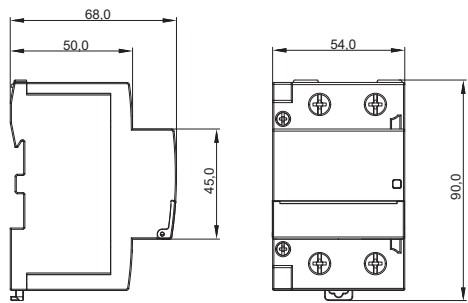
Габаритные размеры контакторов 100 А, 2P / Figure 5 – Overall dimensions of 100 A, 2P contactors
